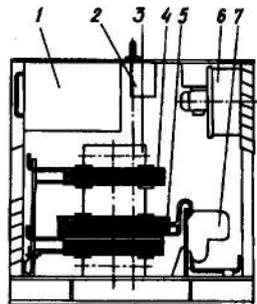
Зовнішній вигляд трансформатора ТДФ-1001 для автоматичного зварювання під флюсом
